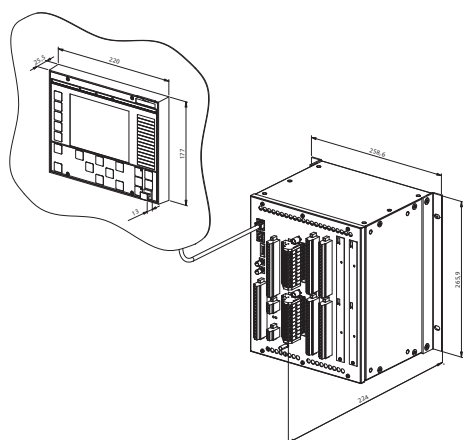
Montage mural d'un boîtier 6U demi 19" avec deux supports de fixation et IHM locale retirée
